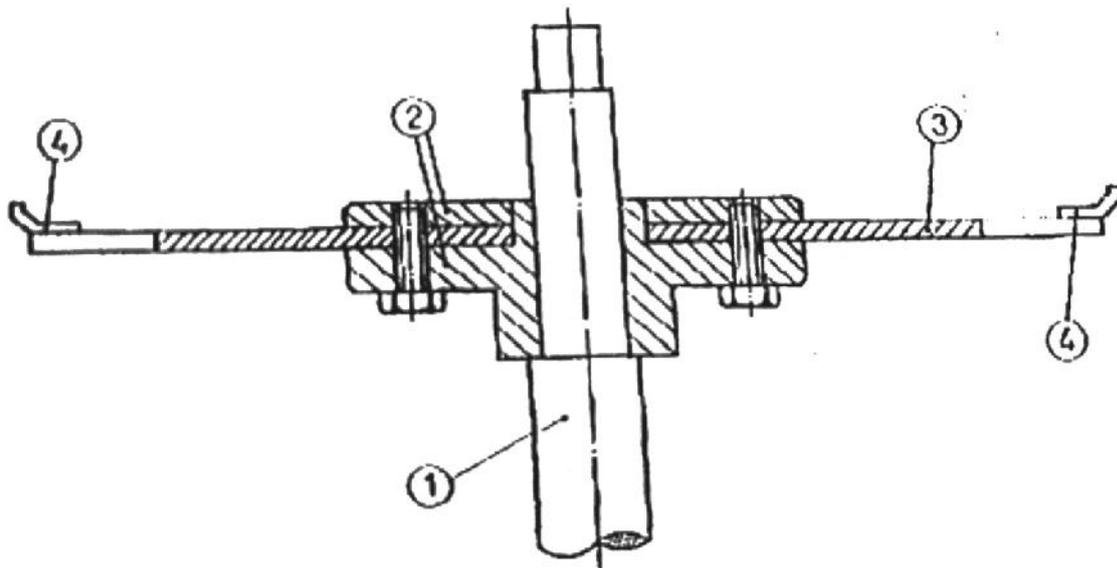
Dessin technique du plateau transporteur de boites et couvercles
